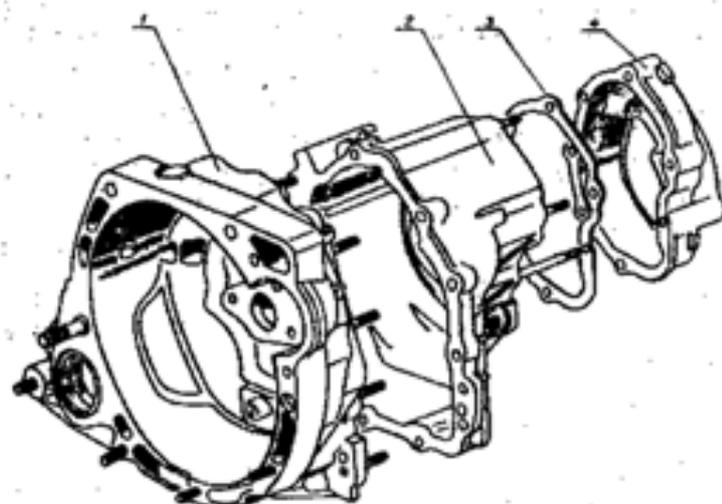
Корпусные детали коробки передач: 1 - картер сцепления; 2 - картер коробки передач; 3 - прокладка; 4 - крышка задняя
